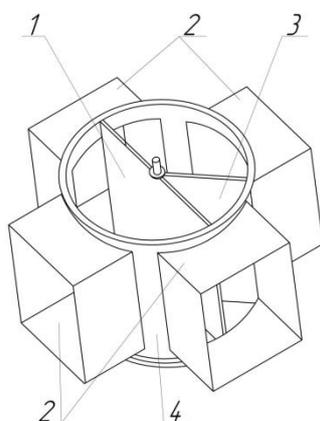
Конструктивно-технологічна схема повітрообмінника: 1 – рухома заслінка; 2 – патрубки; 3 – нерухома заслінка; 4 – циліндричний корпус (камера змішування)
